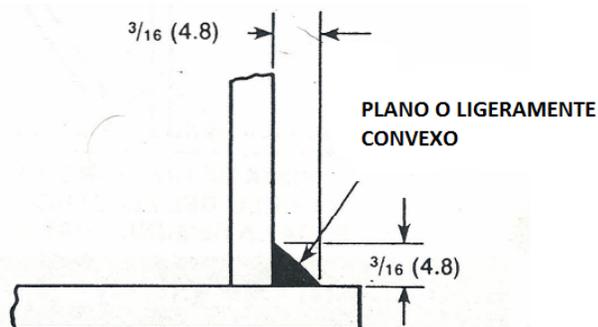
SOLDADURA PARA ENSAYO DE FRACTURA
